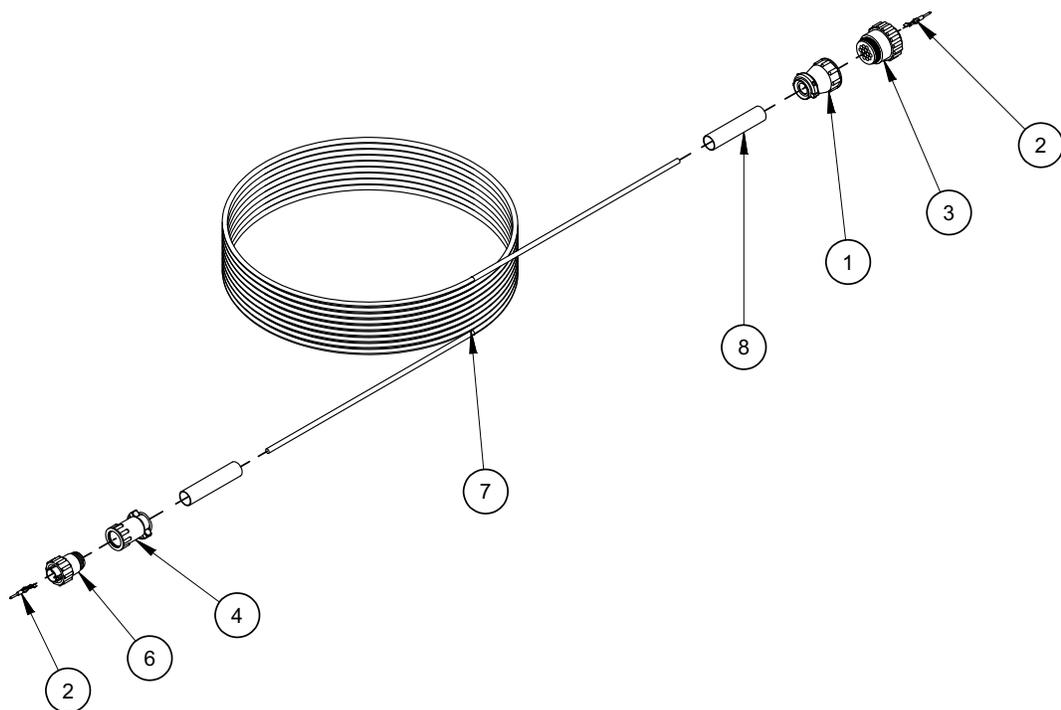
14-контактные пластиковые соединители кабеля блока питания в сборе (кат. № 72101)
